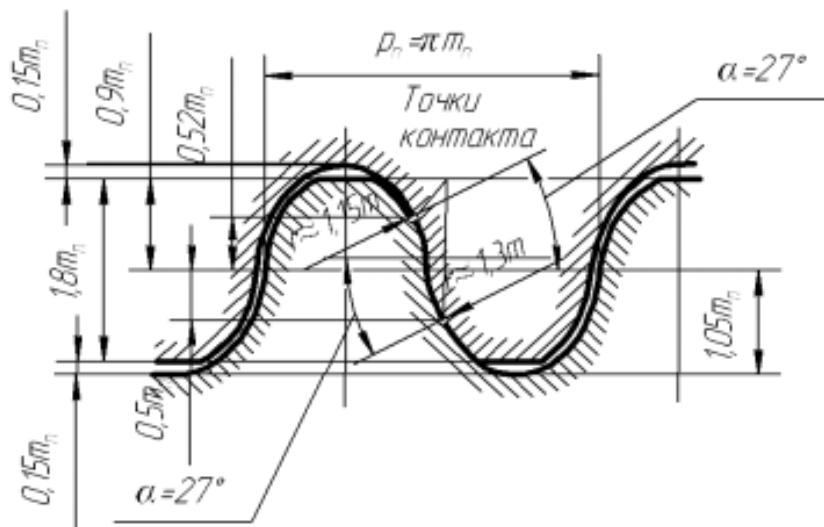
Исходный контур зубьев шестерни и колеса для передачи Новикова с двумя линиями зацепления.
